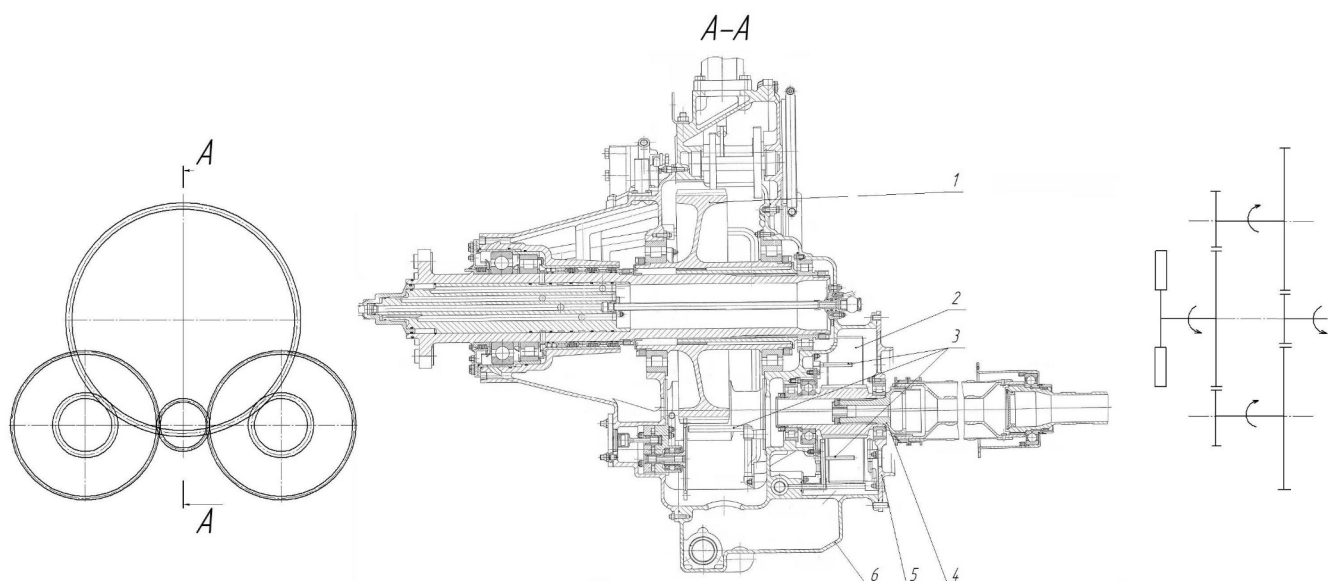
Простой несоосный редуктор СТ7-9: 1 - колесо с косозубым цилиндрическим зацеплением; 2- два колеса с прямозубым цилиндрическим зацеплением; 3 - масляные форсунки; 4 - центральная цилиндрическая шестерня; 5 - носок; 6 – корпус
